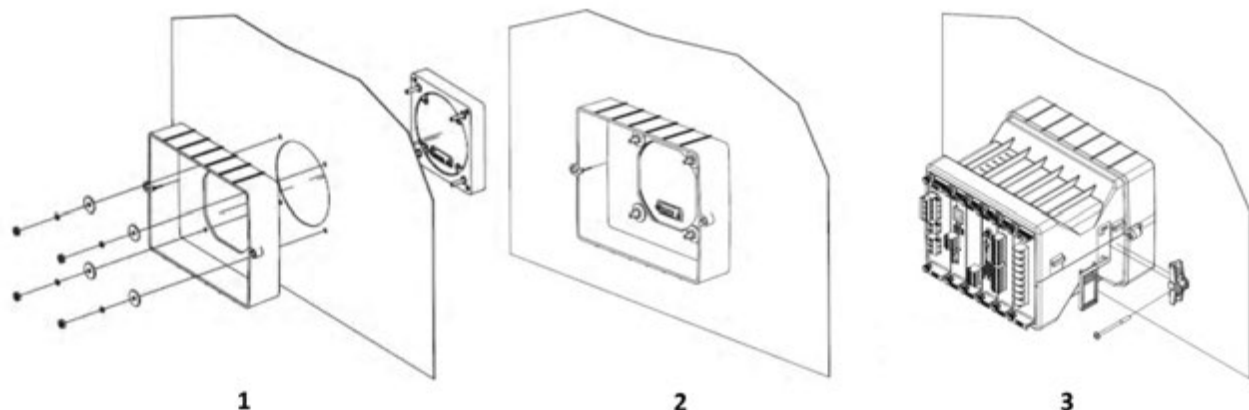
Монтаж РМ180 (прямоугольный или круглый вырез)
